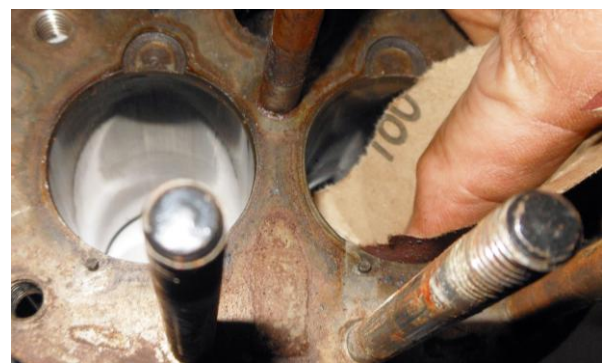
Зачистка рабочей поверхности цилиндра наждачной бумагой
